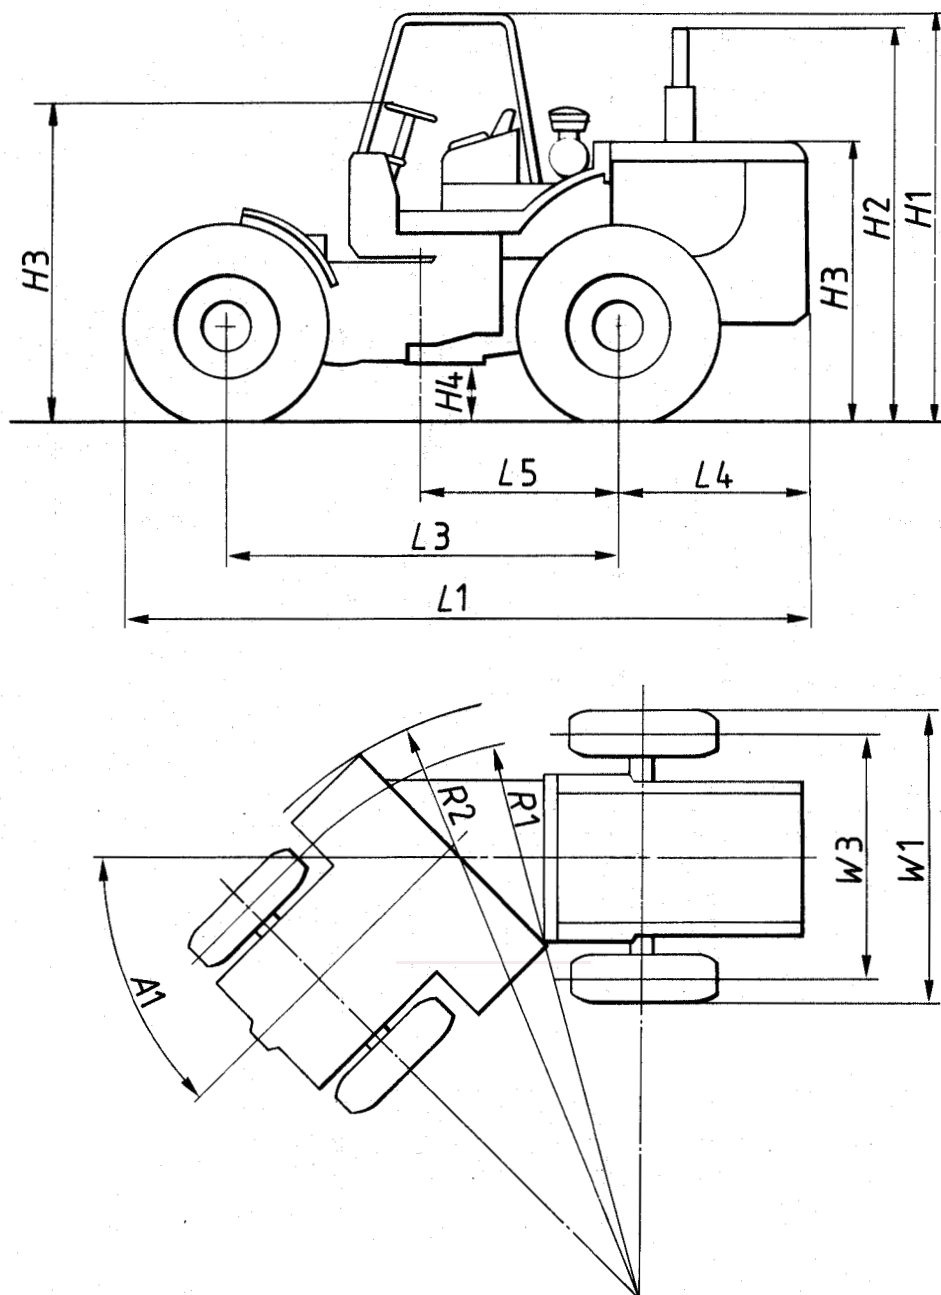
Dimensions de l'engin de base (tracteur à roues)
